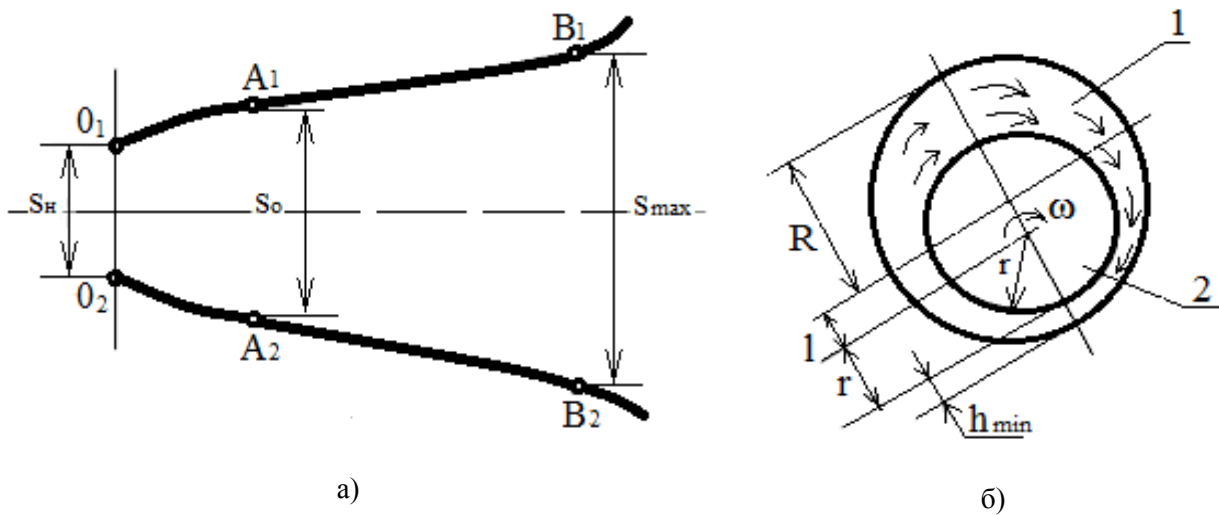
Схема процесса изнашивания сопряжения «вал-подшипник»: а – случай изменения зазора в сопряжении; б - состояние вала в подшипнике. 1 - вал; 2-подшипник;  $S_n$  – начальный зазор;  $S_o$  – оптимальное состояние зазора;  $S_{max}$  – предельный зазор;  $h_{min}$  - минимальное значение толщины масляного слоя;  $R, r$  – радиус вала и подшипника (втулки);  $e$  – абсолютный эксцентриситет.
